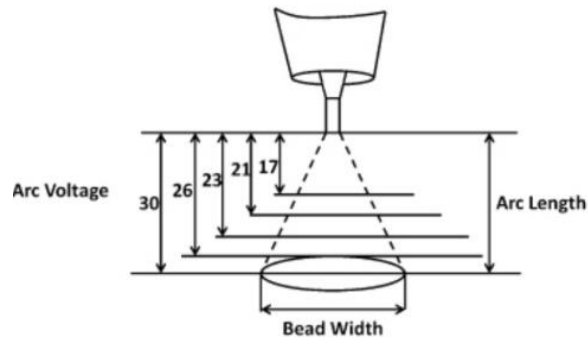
Efecto de la distancia de la punta con el ancho del cordón de soldadura.
